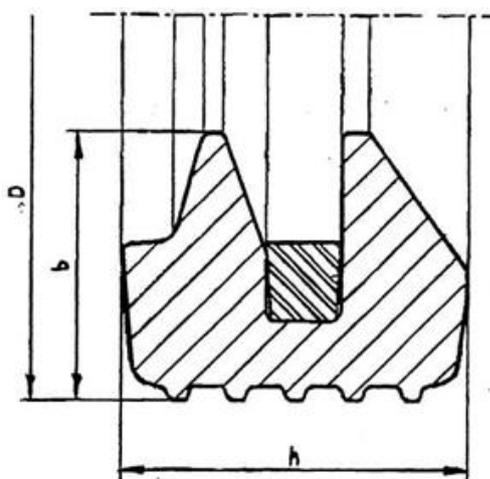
Уплотнительного кольца двухлепесткового типа
